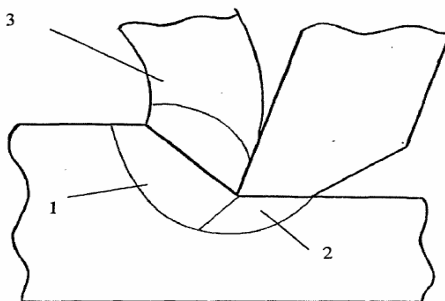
Схема оброблення деталі різцем. 1 — зона деформації металу перед ріжучою кромкою; 2 — зона контакту поверхневого шару деталі із задньою поверхнею інструменту; 3 — зона контакту стружки з передньою поверхнею інструменту
